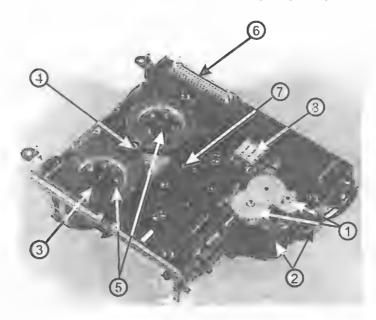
1— шестерни привода микролифта; 2— электромоторы; 3— шасси ЛПМ; 4— пассик; 5— маховики; 6— соединитель; 7— плата управления механизма реверса; 8— шлейф
